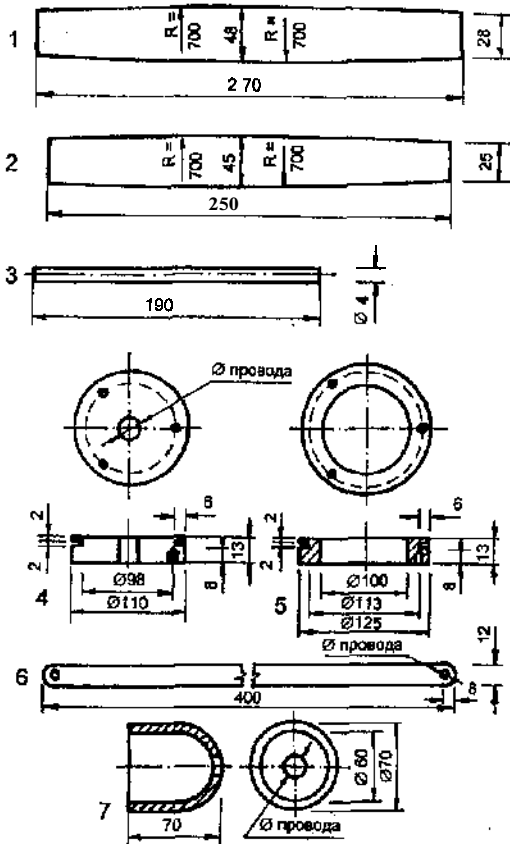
Детали люстры из облицовочного шпона: наружная (1) и внутренняя (2) пластинки; 3 - стержень; верхний (4) и нижний (5) держатели пластинок; 6 - распорка; 7 - чашка потолочная
